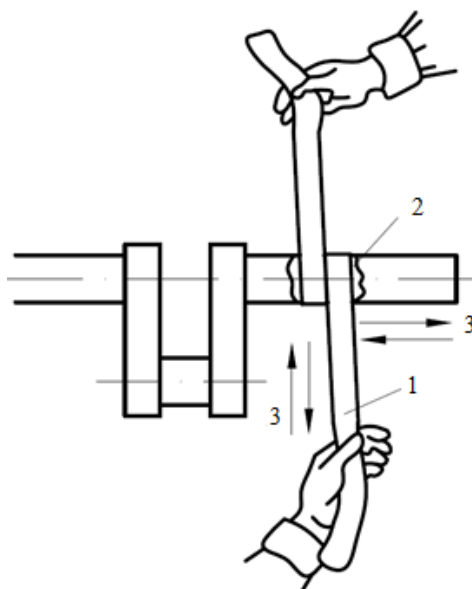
Шліфування шийки вала за допомогою ремня:
